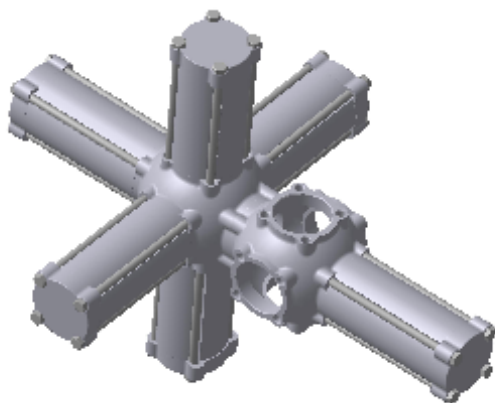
Багатокамерний вибухово-ударний контейнер для сумісного багатостадійного дроблення твердосплавних відходів
